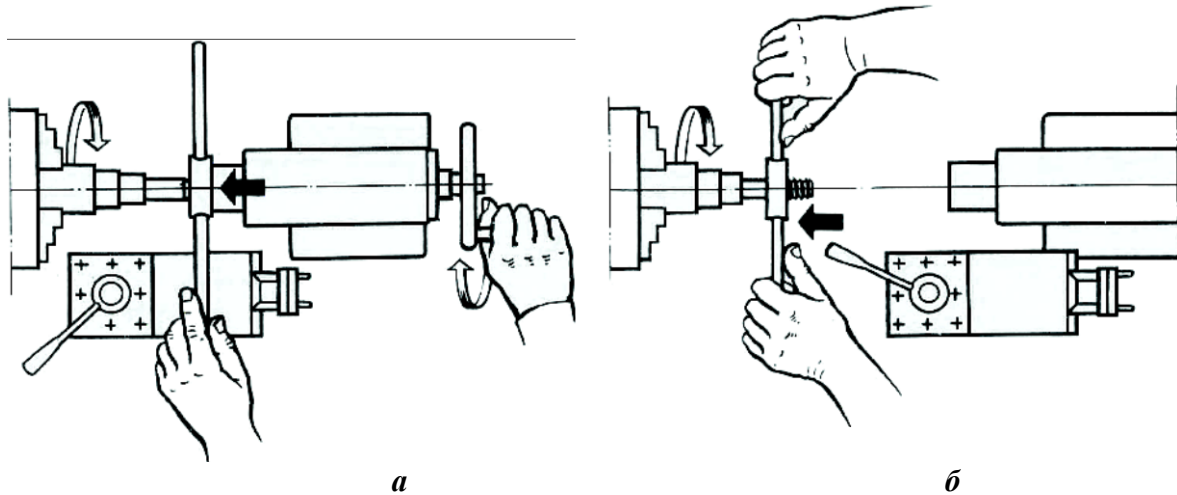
Нарізування різьби плашкою на токарному верстаті
